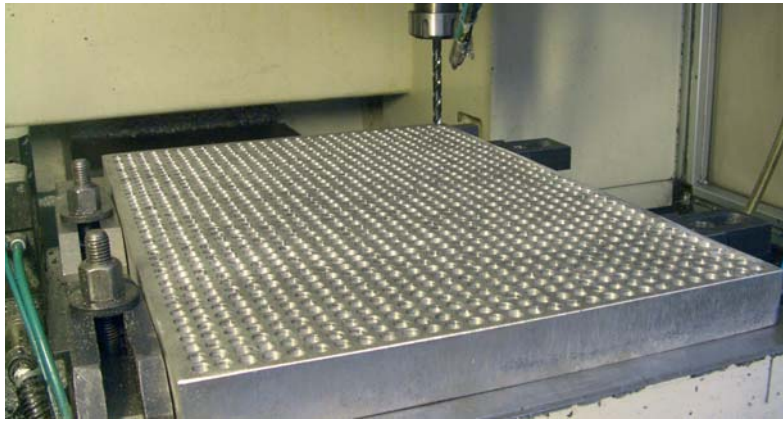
Bohrungsbearbeitung einer partikelverstärkten Aluminiumlegierung
